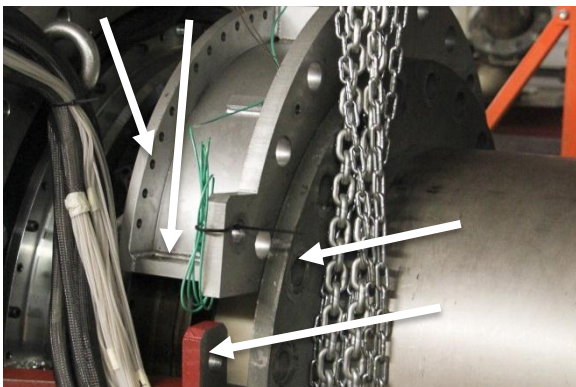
Kennzeichnung der zu entfernenden Schrauben für die Demontage des vorderen Einlaufes
